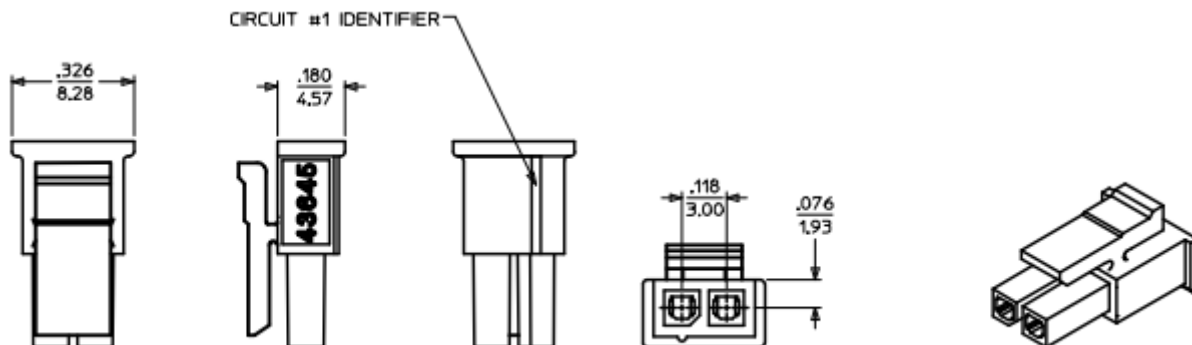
Conector da Fonte de Alimentação para Bridge Master
